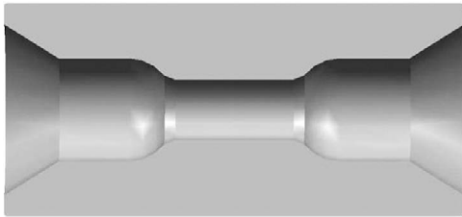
Kolbenbolzen mit profilierter Innenform
